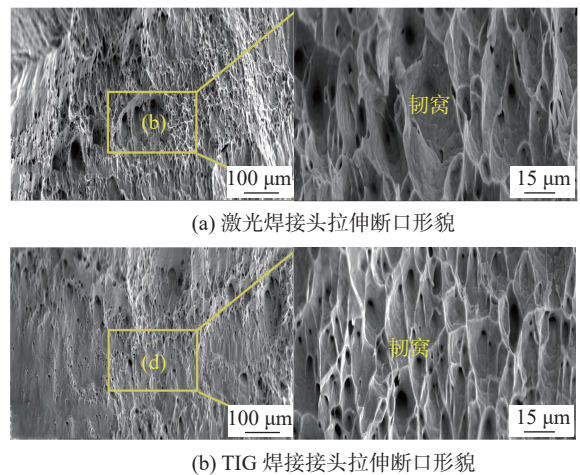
两种焊接接头的拉伸试验断口形貌
